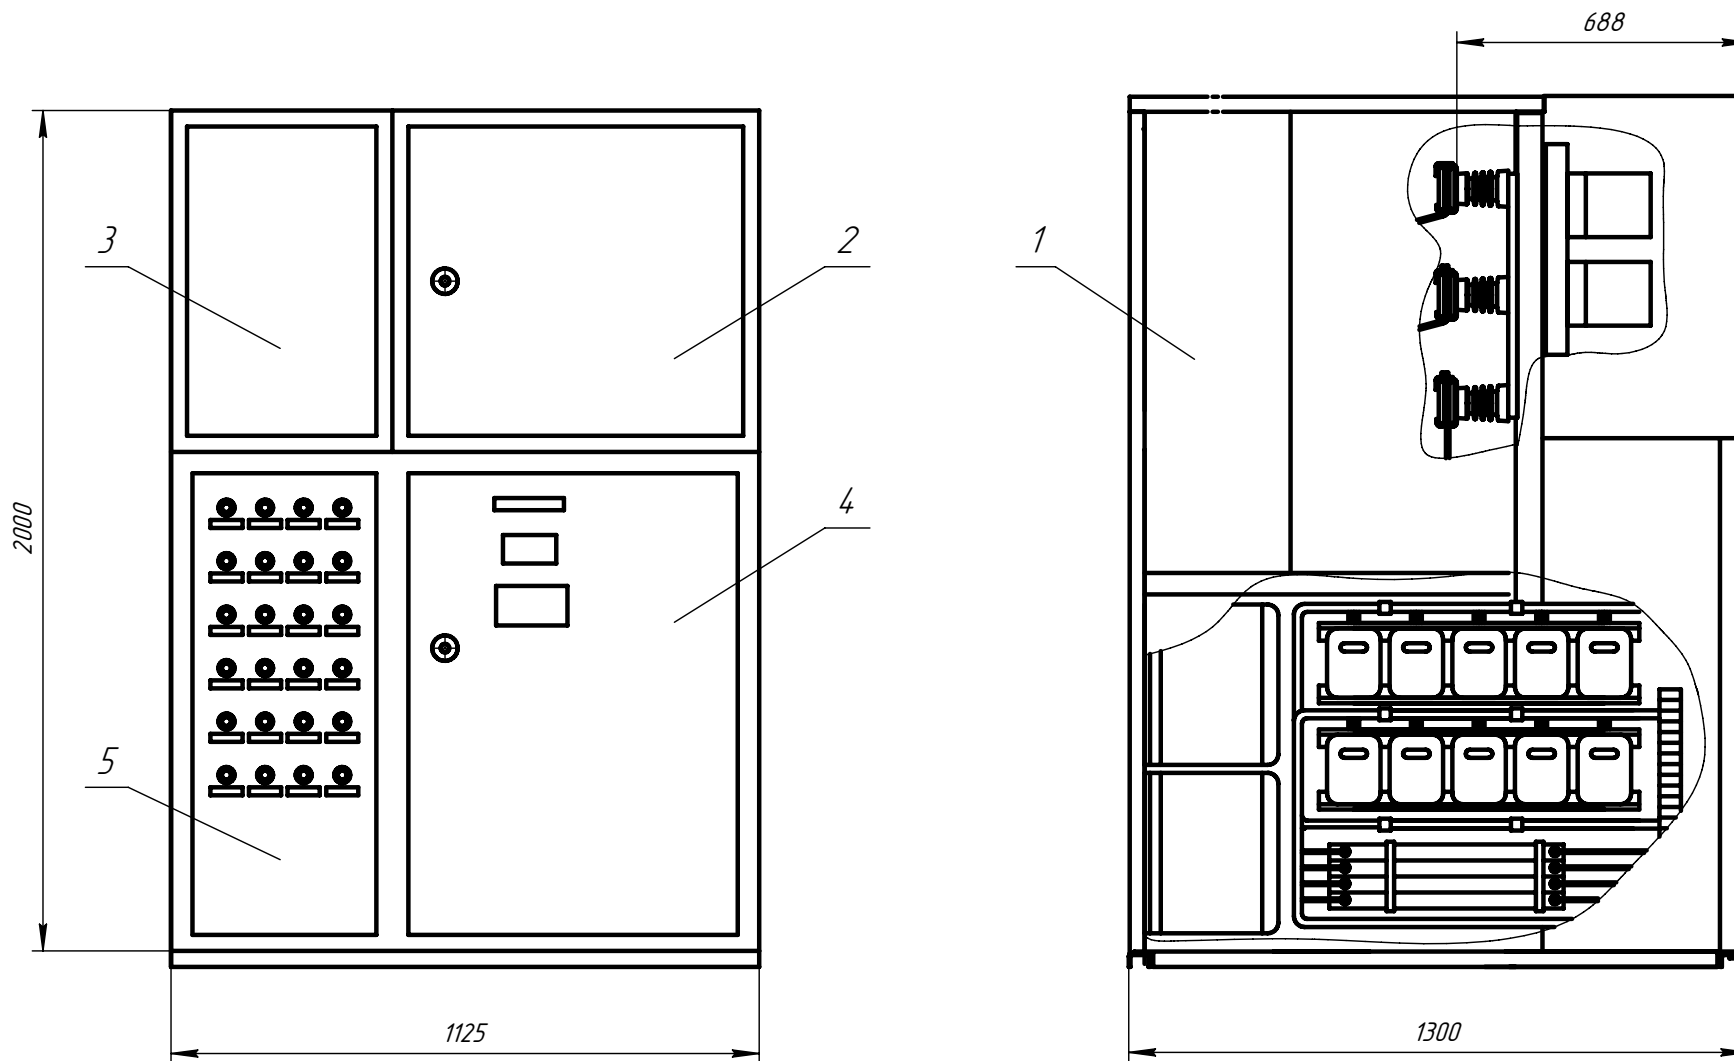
Габаритные, установочные, присоединительные размеры шкафов.
